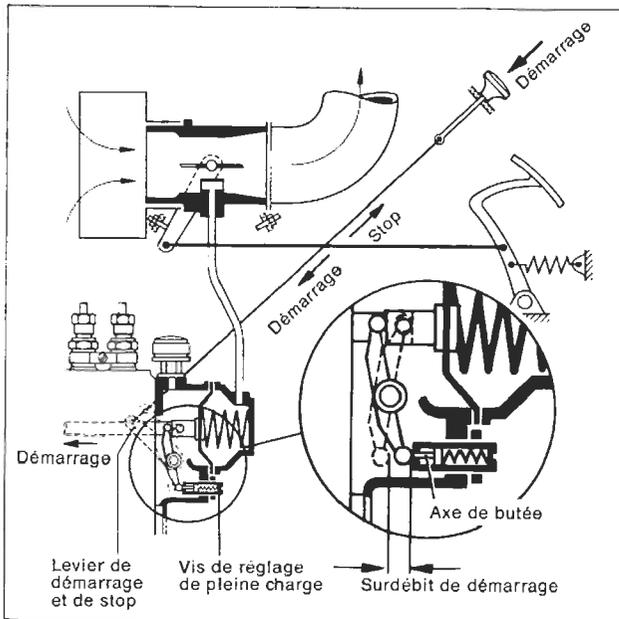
Ensemble membrane du régulateur pneumatique avec butée de tige de réglage incorporée pour pleine charge et surdébit de démarrage.
